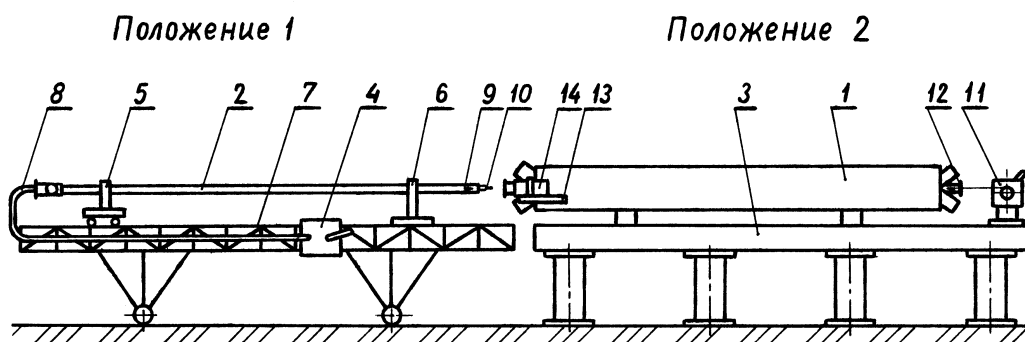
Схема ступени стенда установки камер в магниты: 1 — дипольный магнит; 2 — вакуумная камера; 3 — контрольно-сборочный стол; 4 — гидронасос; 5 — каретка; 6 — опора; 7 — передвижная тележка; 8 — дюритовые шланги; 9 — проушина; 10 — приспособление для осадки; 11 — лебедка; 12 — второй фланец камеры; 13 — кронштейн для крепления насоса; 14 — насос ПВИГ-100.
